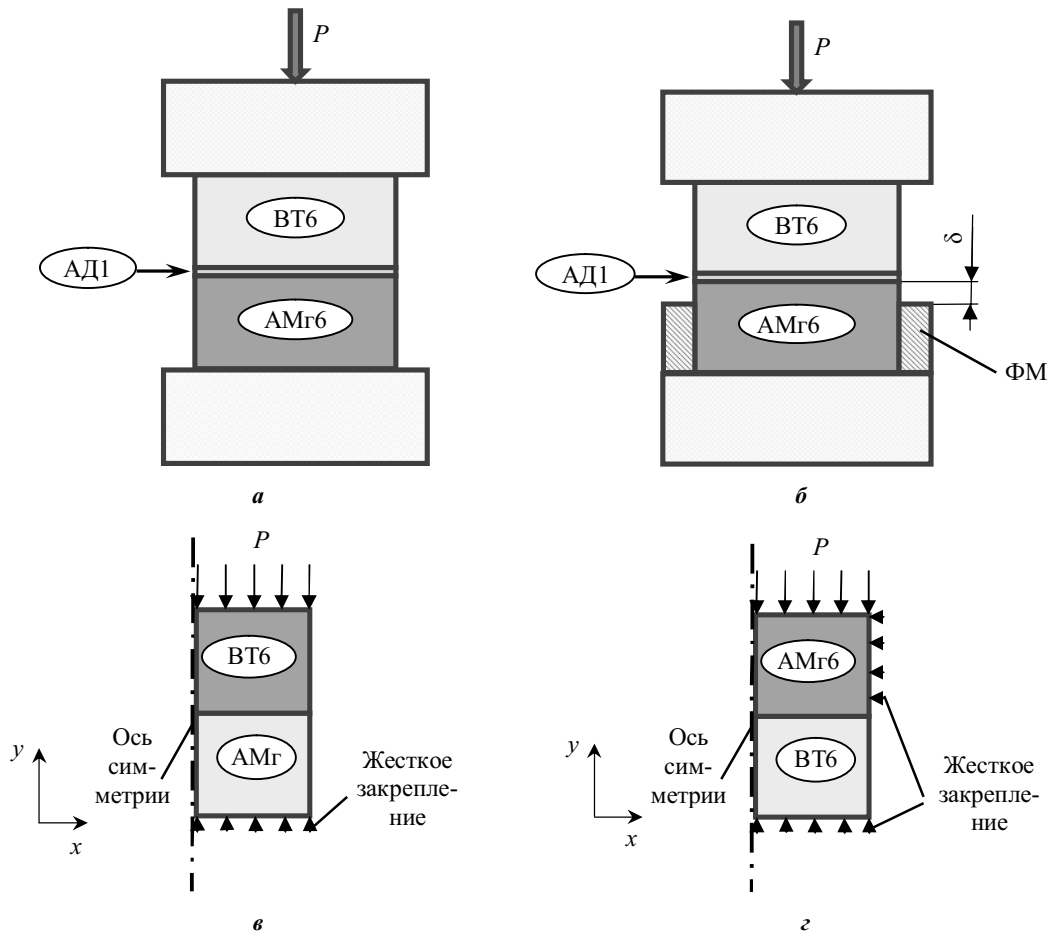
Схемы ДСВ (*a, б*) и расчетные модели (*в, з*): *a, в* – сварка без ФМ; *б, з* – сварка с ФМ; *x, y* – оси координат
